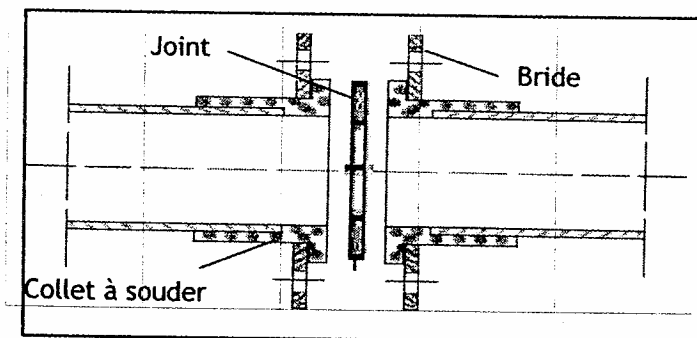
Assemblage tube cuivre 1 tube PVC par brides
